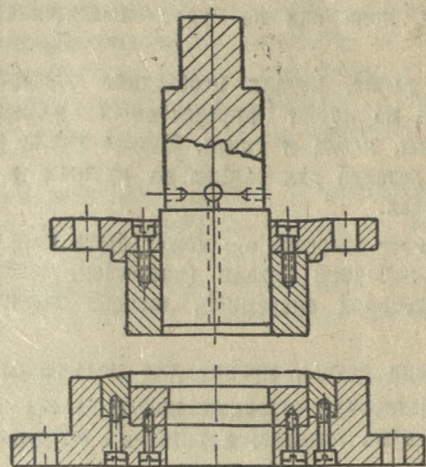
Комбинированный штамп для вытяжки и вырубки
